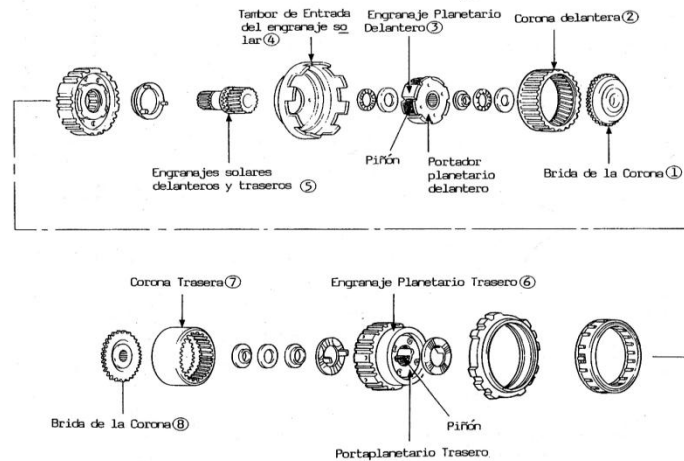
Tren de Engranajes Planetarios Delantero y Trasero.
